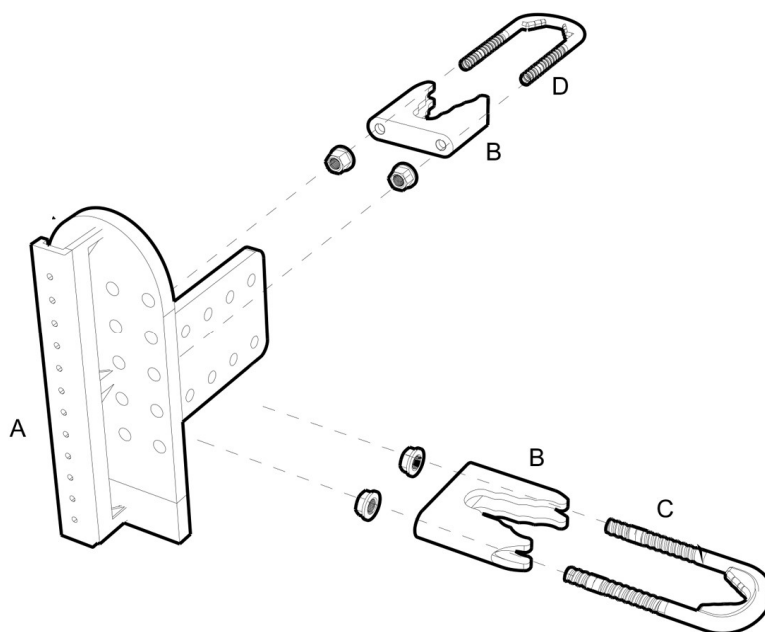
Desenho Técnico da montagem da Parte Ativa do produto
